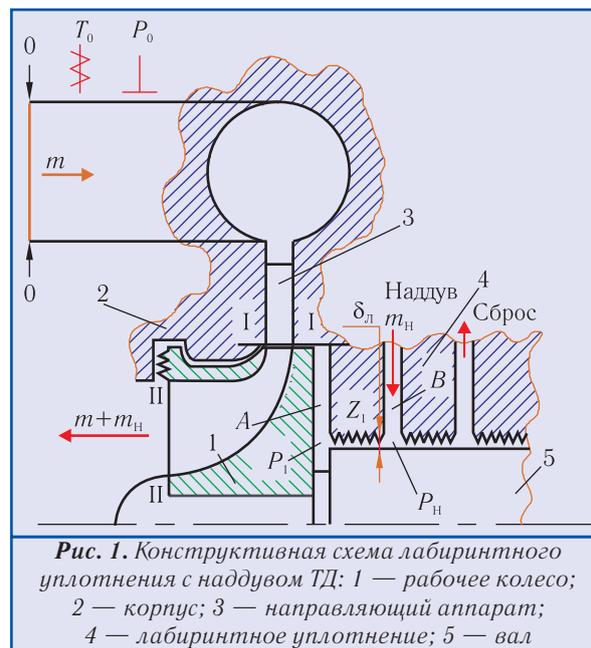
Конструктивная схема лабиринтного уплотнения с наддувом ТД: 1 — рабочее колесо; 2 — корпус; 3 — направляющий аппарат; 4 — лабиринтное уплотнение; 5 — вал
